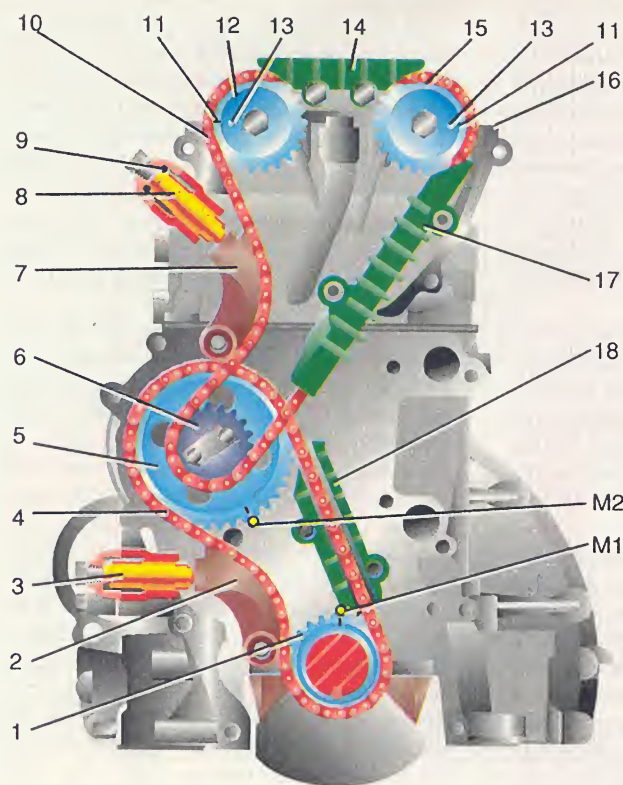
Привод распределительных валов: 1 – звездочка коленчатого вала; 2 – башмак гидронатяжителя нижней цепи; 3 – нижний гидронатяжитель; 4 – нижняя цепь; 5 – ведомая звездочка промежуточного вала; 6 – ведущая звездочка промежуточного вала; 7 – башмак гидронатяжителя верхней цепи; 8 – верхний гидронатяжитель; 9 – шумоизолирующая резиновая шайба; 10 – верхняя цепь; 11 – установочная метка на звездочке; 12 – звездочка распредвала впускных клапанов; 13 – установочные штифты; 14 – верхний успокоитель цепи; 15 – звездочка распредвала выпускных клапанов; 16 – верхняя плоскость головки цилиндров; 17 – средний успокоитель цепи; 18 – нижний успокоитель цепи; M1 и M2 – установочные метки на блоке.
